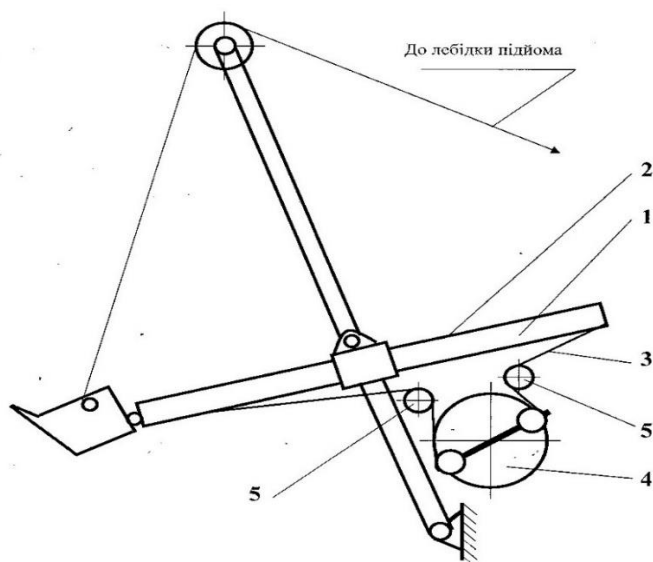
Конструктивна схема механізму натиску ковша екскаватора - прямої механічної лопати.
